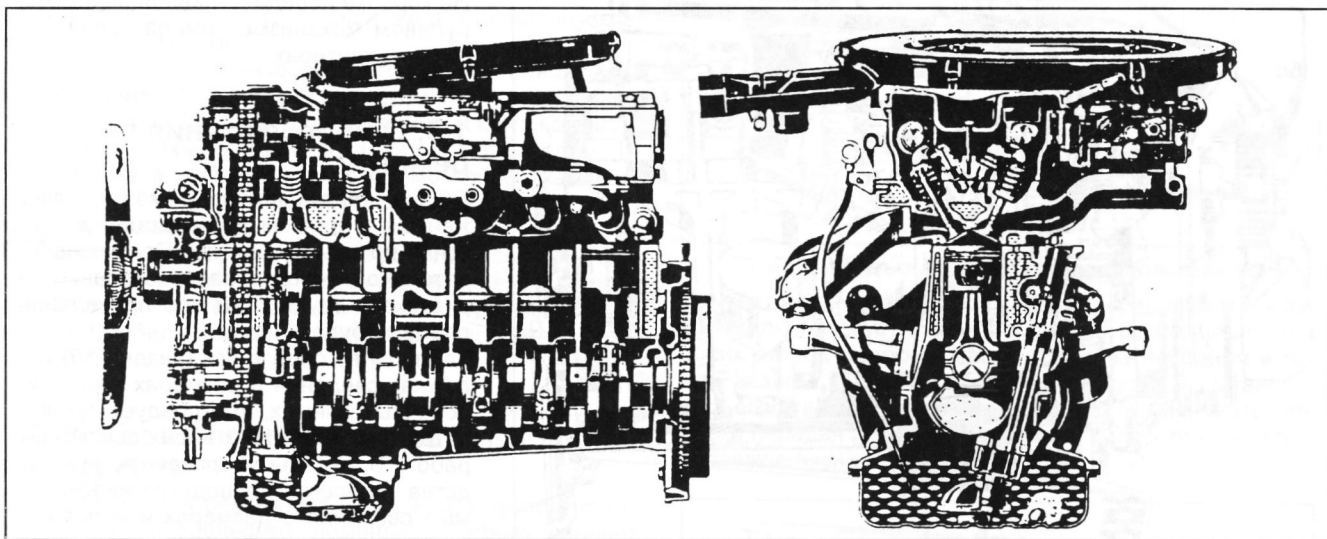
Продольный и поперечный разрезы карбюраторного двигателя M110.
